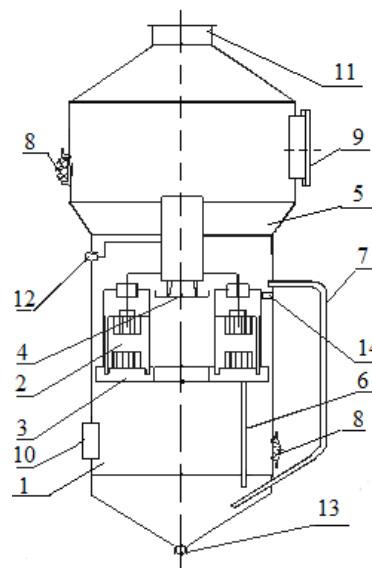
Вихревой аппарат мокрой пылеочистки внедренный на ОАО «Крымский содовый завод»: 1 - корпус; 2 - элемент пылеулавливающий; 3 - полутарелка нижняя; 4 - полутарелка верхняя; 5 - бак распределительный; 6 - патрубок слива; 7 - гидрозатвор; 8 - люк-лаз; 9 - монтажный люк; 10 - патрубок входа газа; 11 - патрубок выхода газа; 12 - патрубок входа воды; 13 - патрубок слива шлама; 14 - уплотнение
